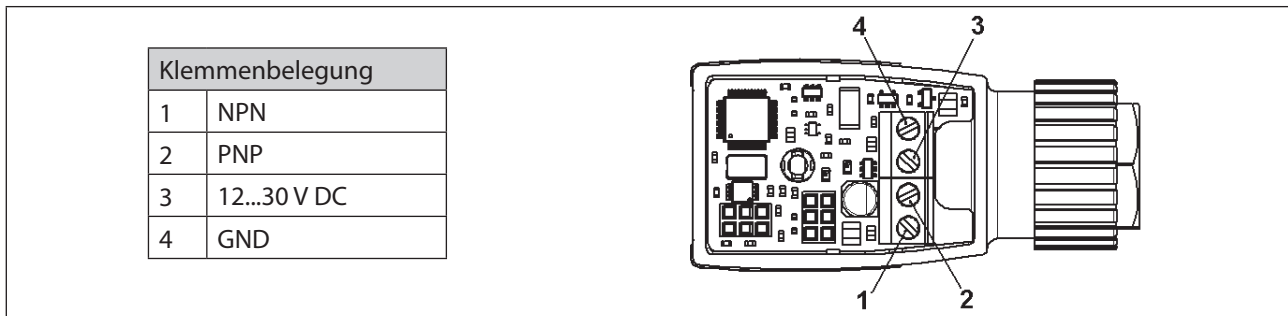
Klemmenbelegung, Ausführung mit Kabelverschraubung
